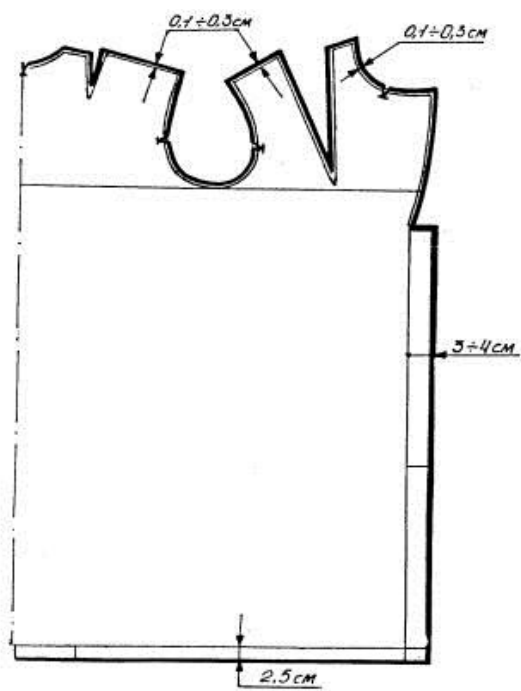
Креслення лекала деталі стану хутряного верху
